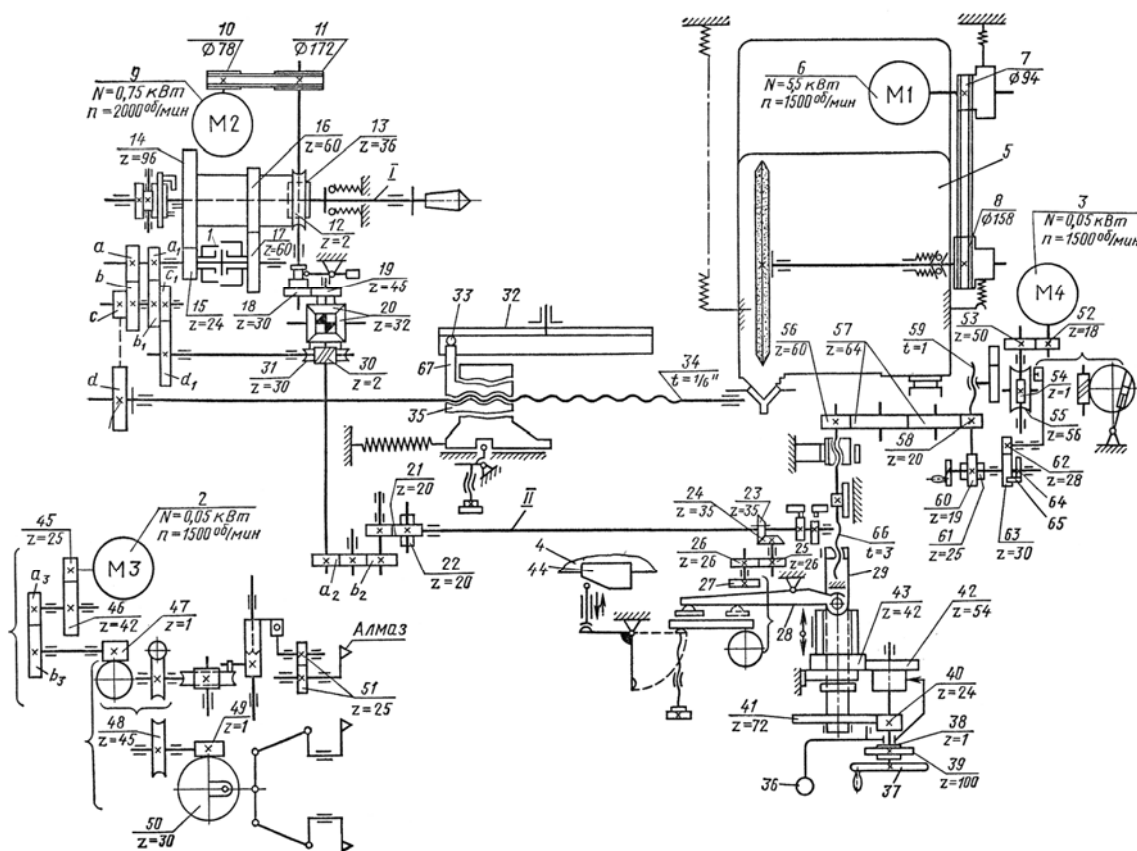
Кинематическая схема резьбошлифовального станка мод. 5822М
